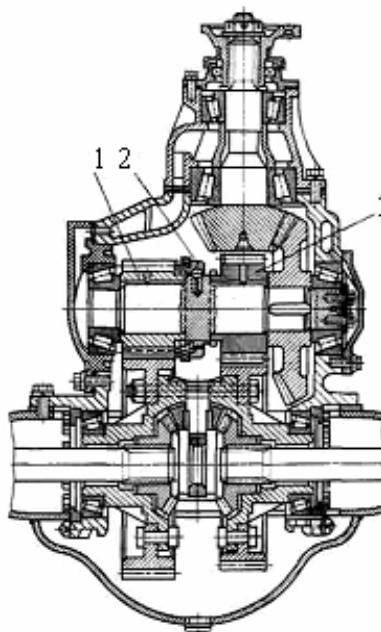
Двоступенева головна передача з циліндричною зубчатою передачею:
